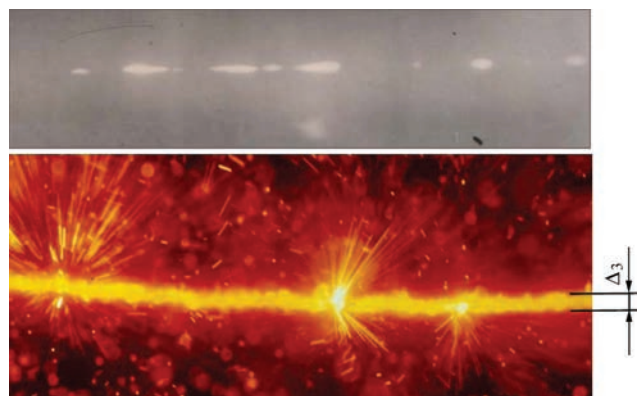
Рентгенограмма искрового зазора при сварке рельсов
